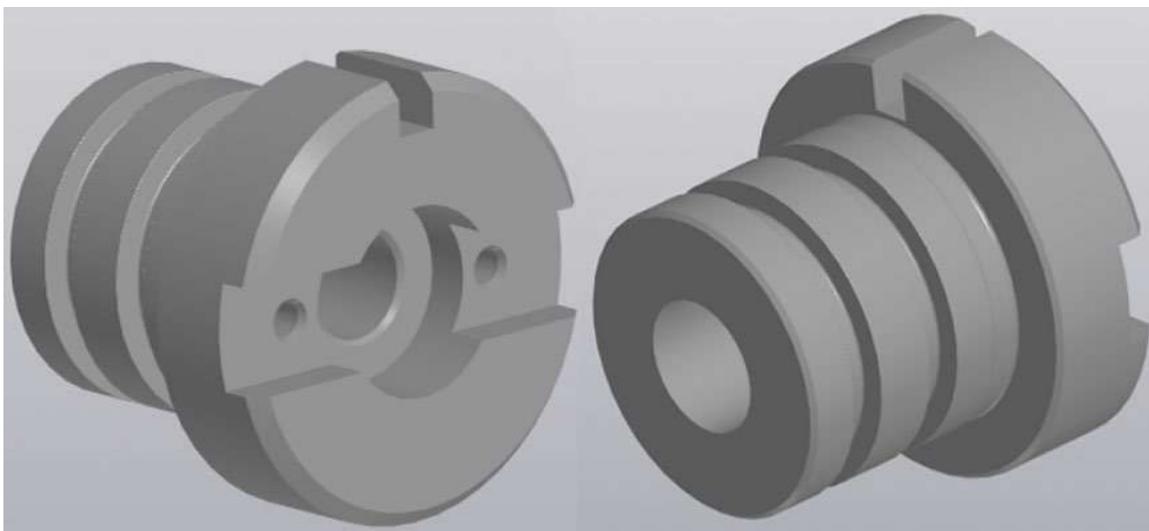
3D модель детали «Втулка гидроцилиндра»
